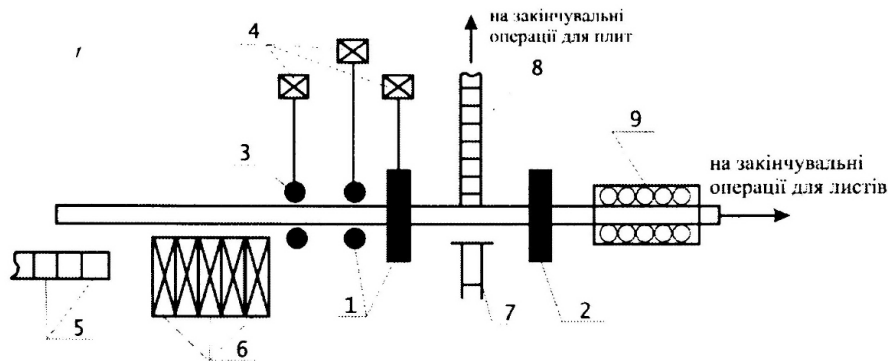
Схема компоновки ТЛ ТСЛ 3600: 1-чорнова реверсивна універсальна кліть кватро; 2-чистова реверсивна кліть кватро; 3-кліть з вертикальними валками (окалиноламах); 4- головні електродвигуни; 5-нагрівальні колодязі; 6-нагрівальні печі; 7-зіштовхвач; 8-шлепер; 9-правильно-загартовуюча машина.
